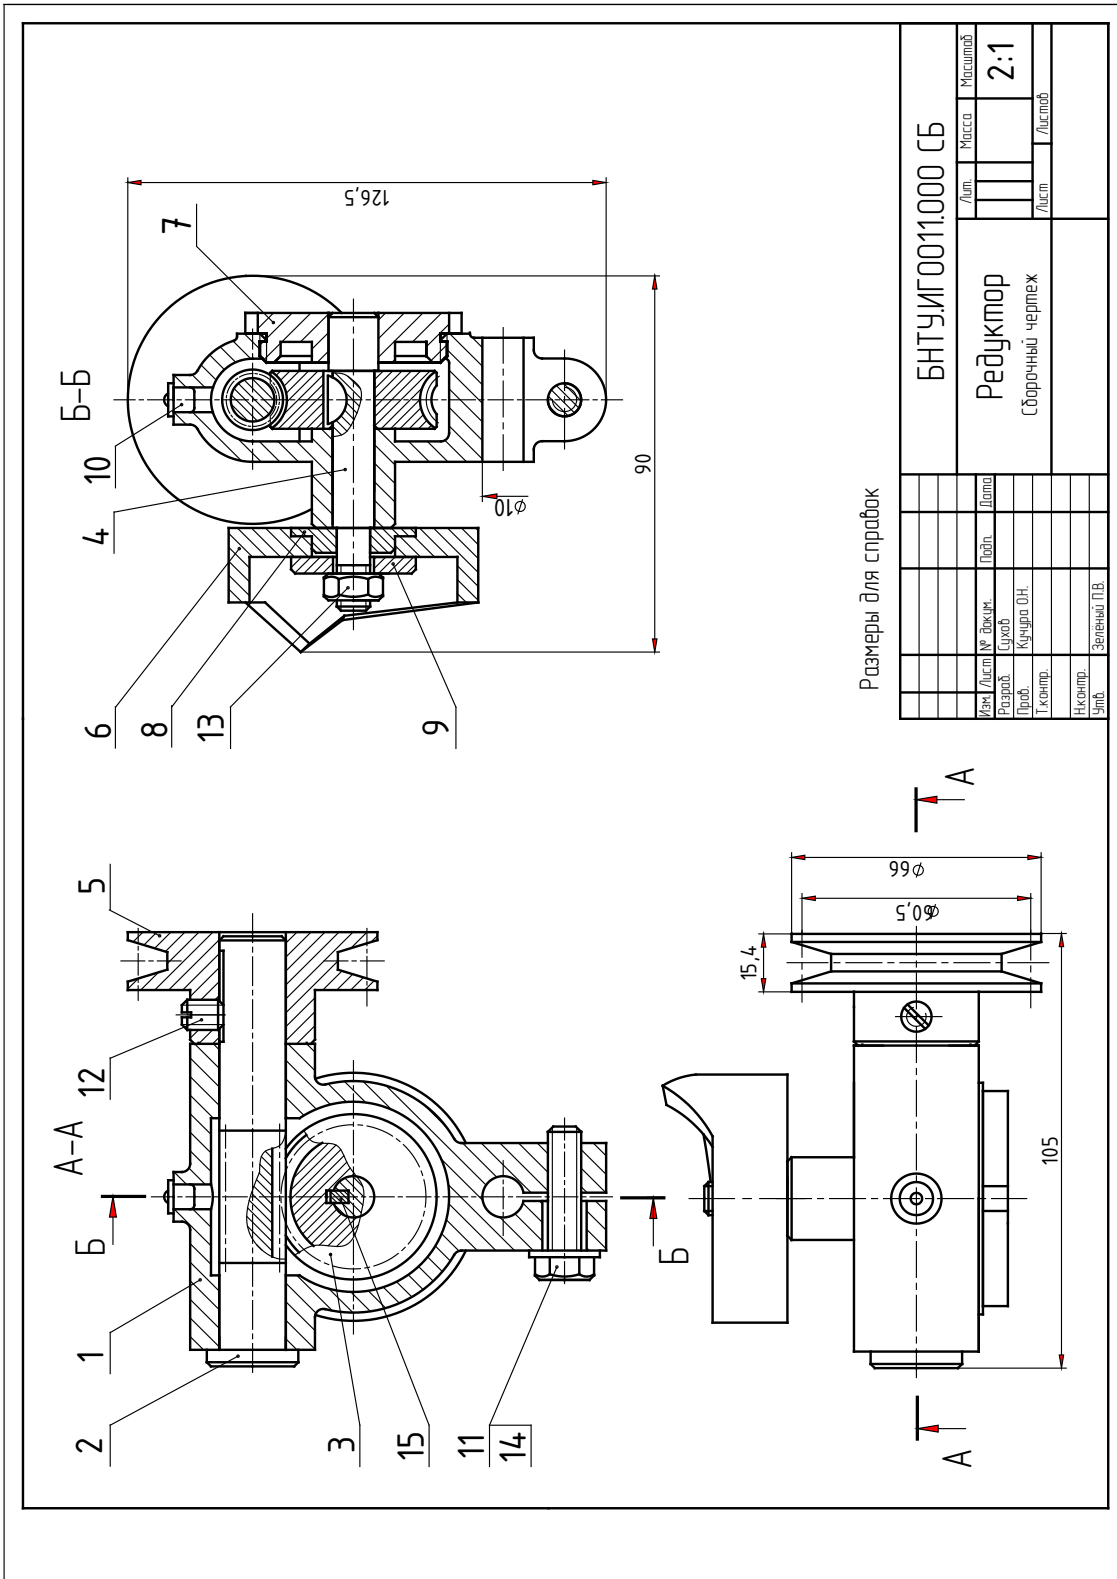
Редуктор червячный (сборочный чертеж)
